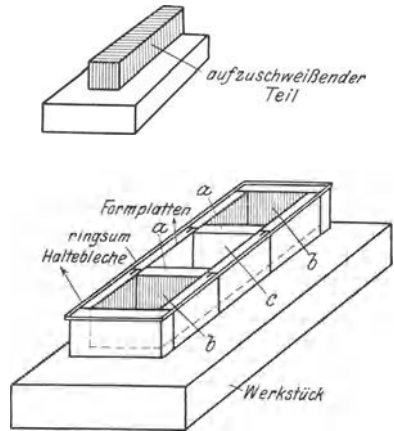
Unterteilung der Schweißstelle in Kammern.
